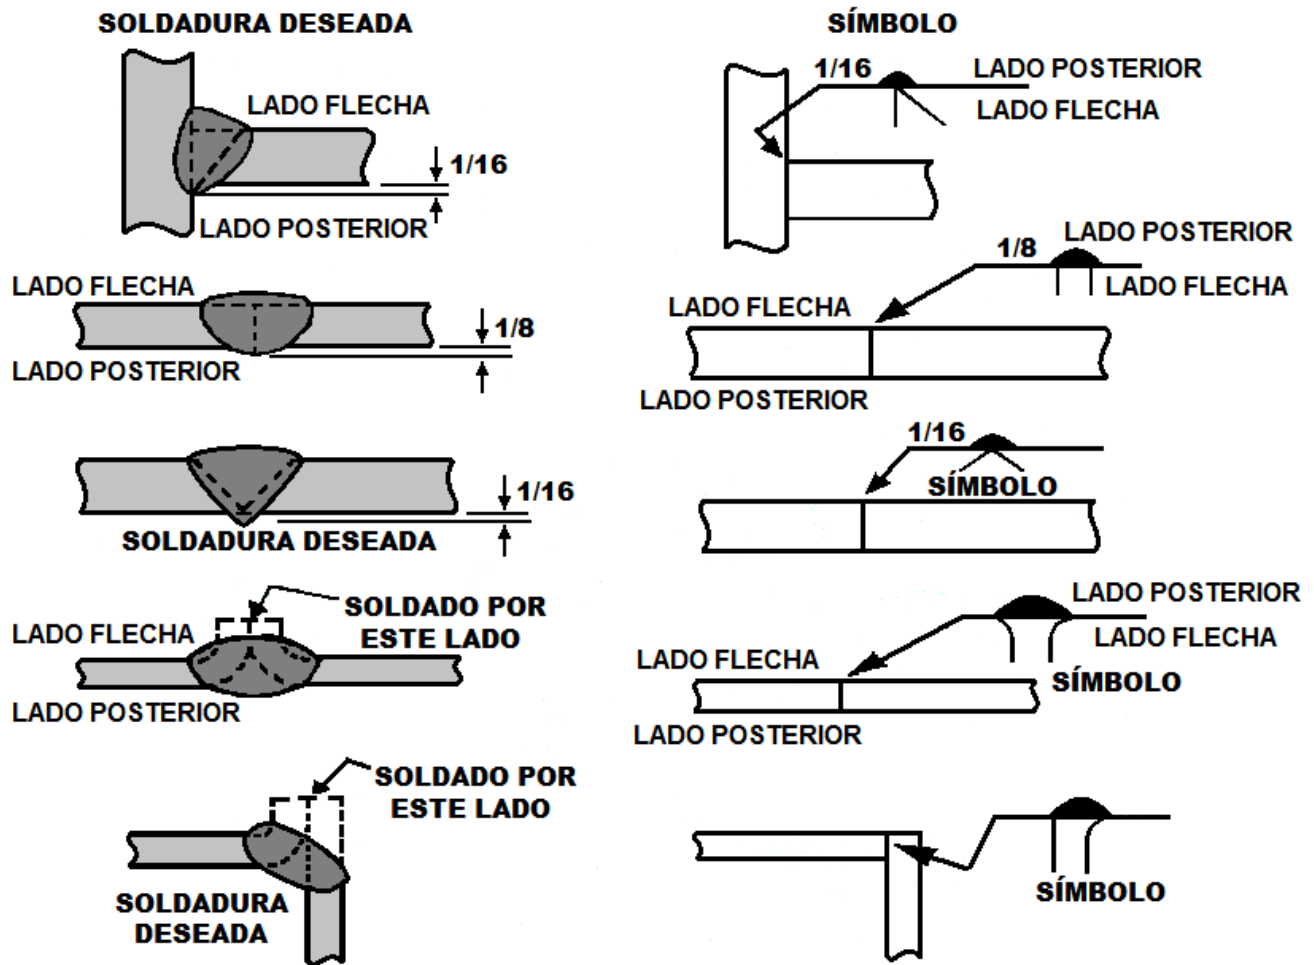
Dimensiones y forma de la soldadura según los símbolos (3, 8, 18, 31)
